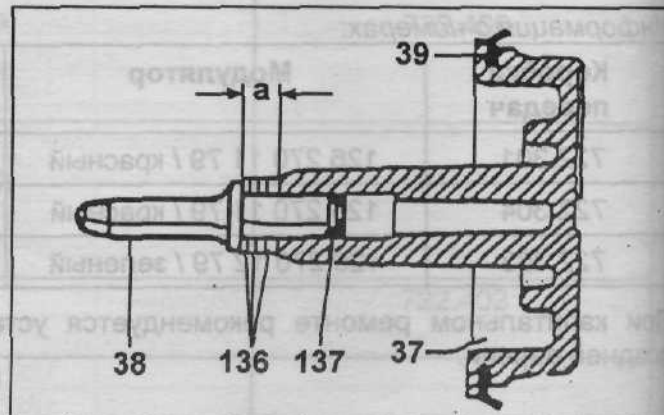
37 - Поршень ленточного тормоза В1; 38 - Шток; 39 - Уплотнение; 136 - Прокладки; 137 - Кольцевое уплотнение.
